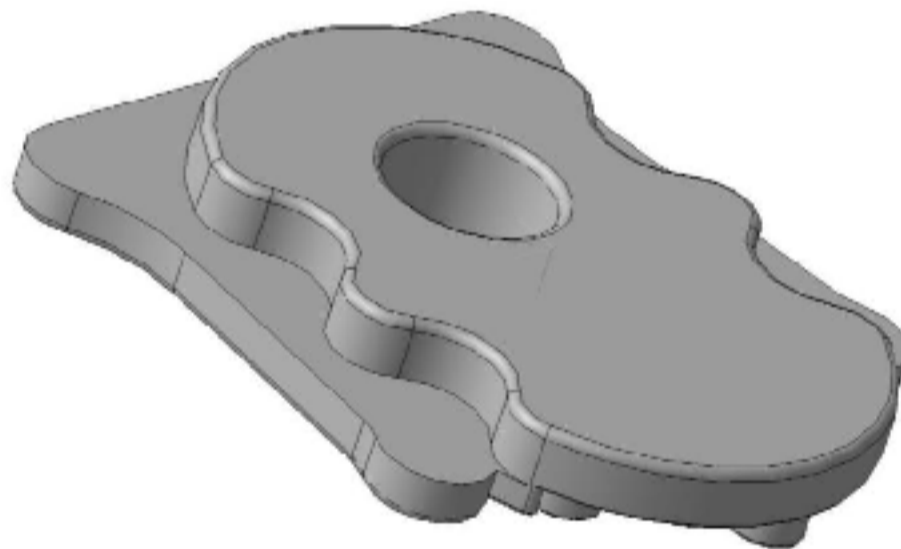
3D-модель заготовки виготовленої литтям в кокіль
